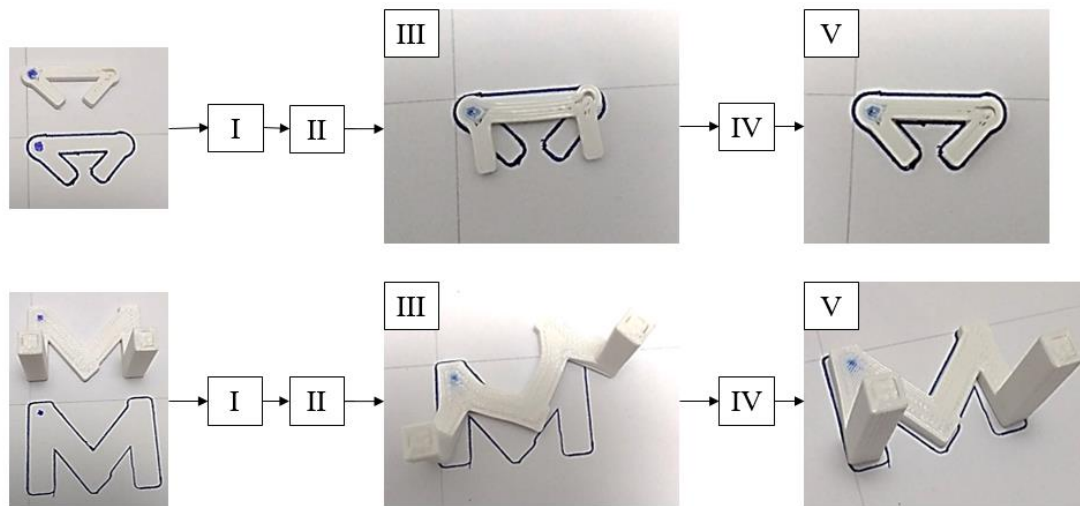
Procedimento realizado em primeiro teste, peças B e C
